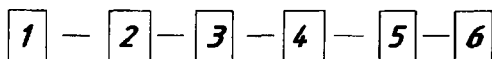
Структура условного обозначения сварного шва
